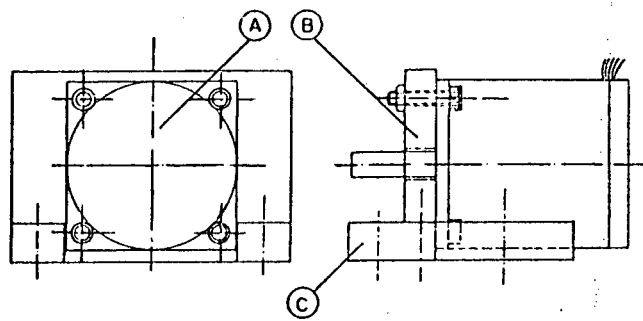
Sistema flangeado usado para fixação do motor do mecânica X.
